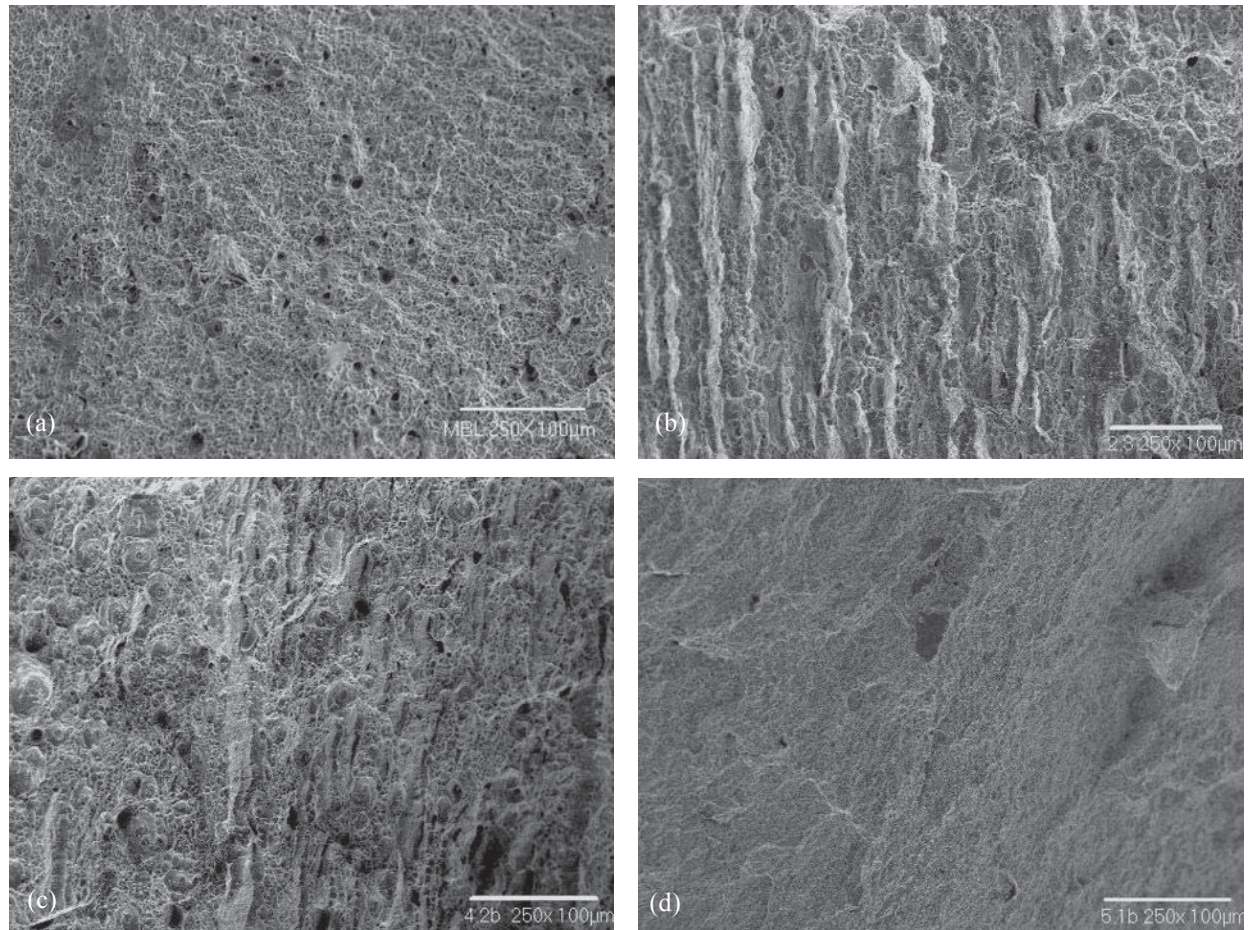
22.- Fractografías del ensayo de tensión con unión en simple V 100x (a) Material base (b) ZAT, soldada sin campo magnético (c) ZAT, soldada con campo magnético (d) ZAT, soldada con campo magnético y variando la orientación del la líneas del campo.
